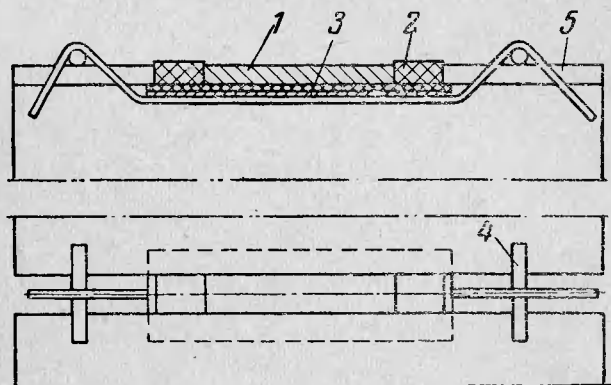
Приспособление для заварки алюминиевых сухарей.
